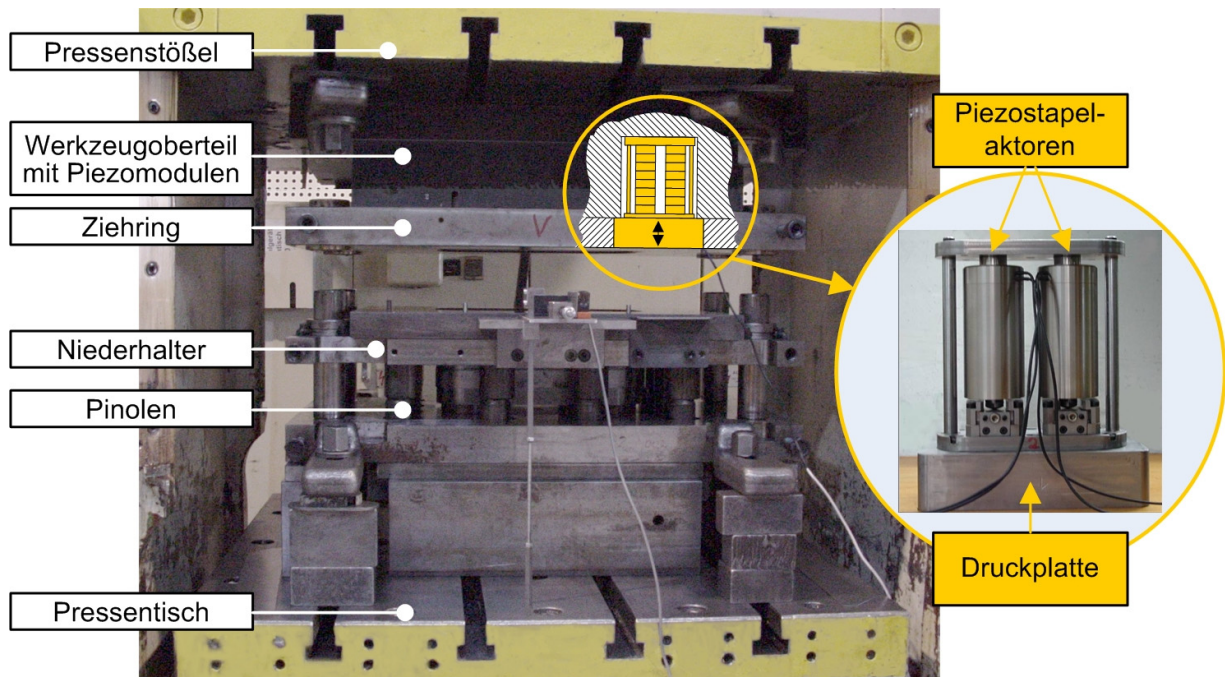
Prinzip piezoaktorisches Ziehwerkzeug [16]
